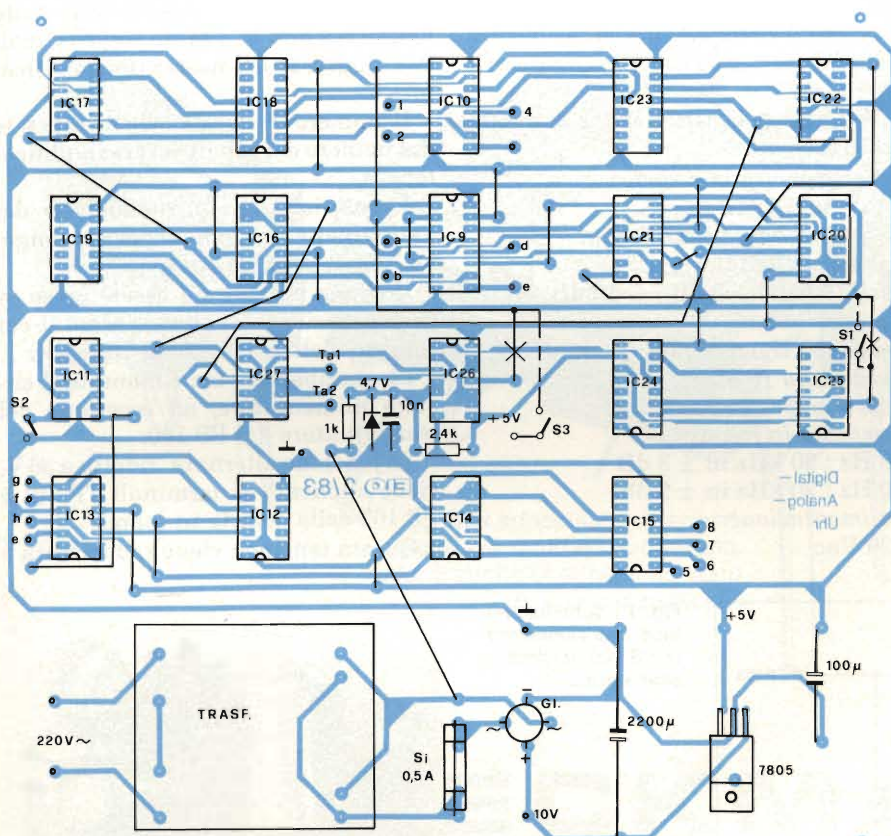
Disposizione dei componenti sul circuito stampato di Fig. 6.
